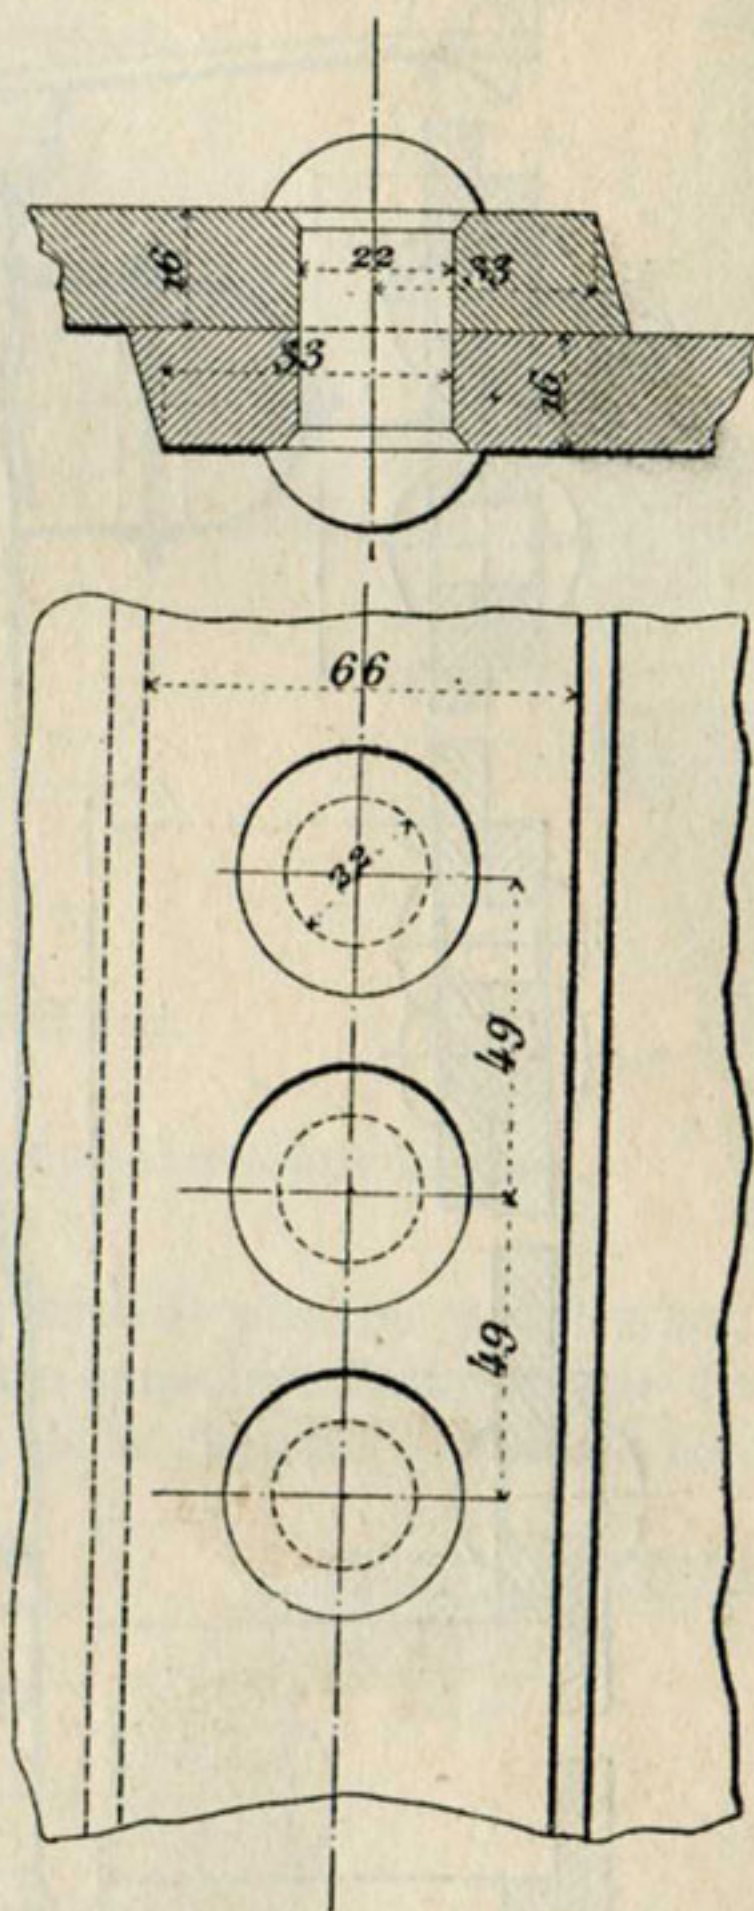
Rivure à recouvrement, avec simple rang de rivets.
